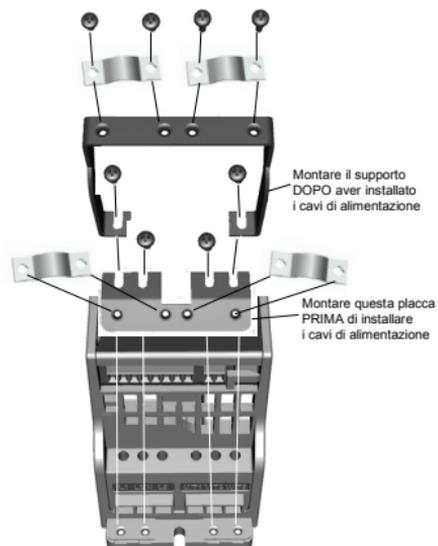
Montaggio della placca PE e del supporto cavi API, MI1-MI3
